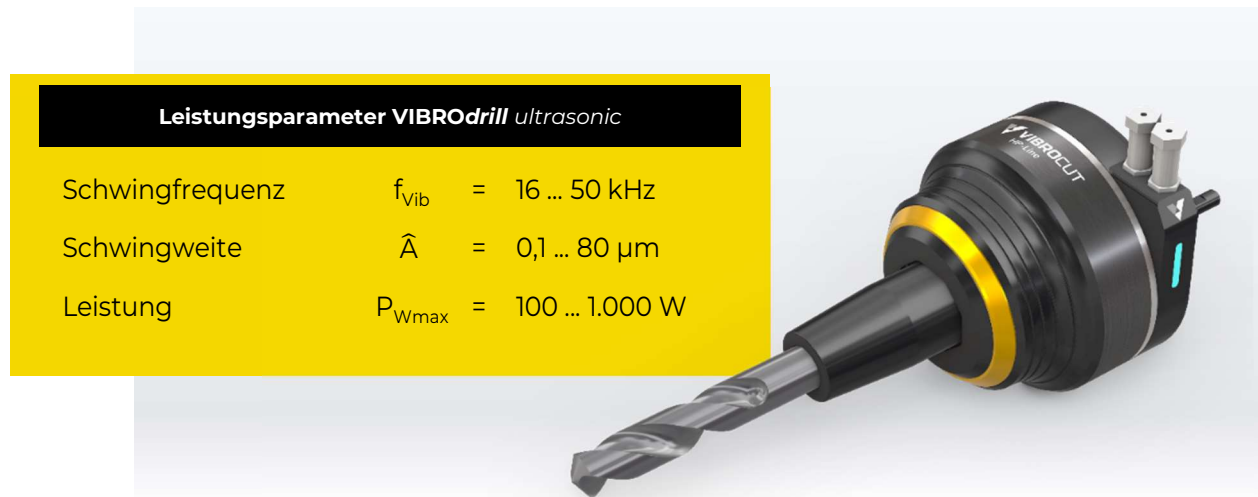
Ultraschall-Werkzeughalter VIBROdrill ultrasonic
